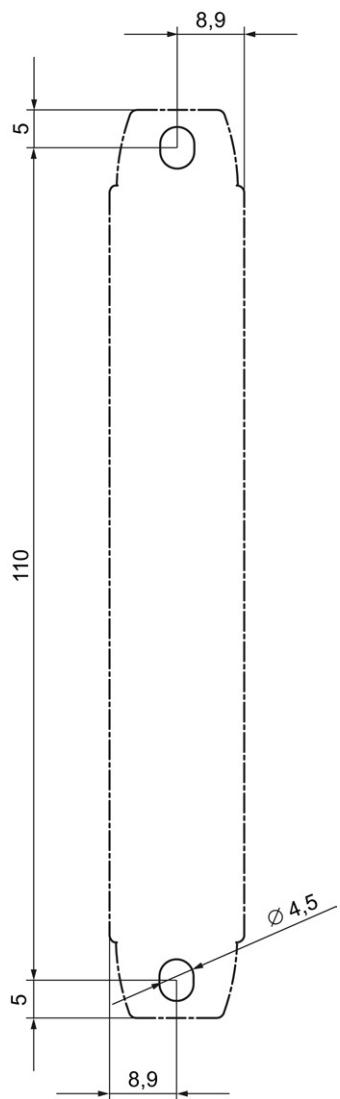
Bohrplan Gehäuse 17,5 mm
